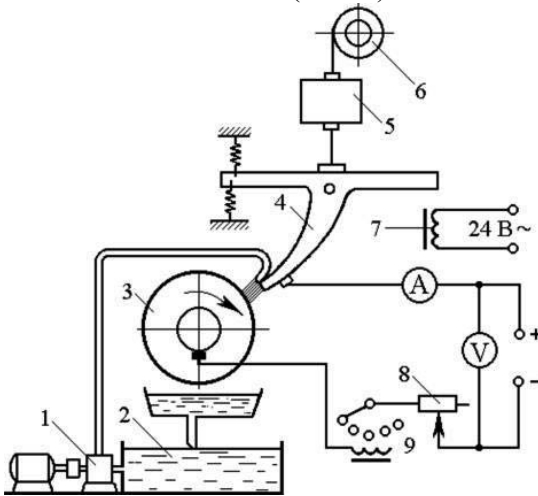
Схема установки для вібродугового наплавлення: 1 – насос; 2 – бак; 3 – деталь; 4 – мундштук; 5 – механізм подачі; 6 – касета з дротом; 7 – вібратор; 8 – реостат; 9 – індукційний резистор
